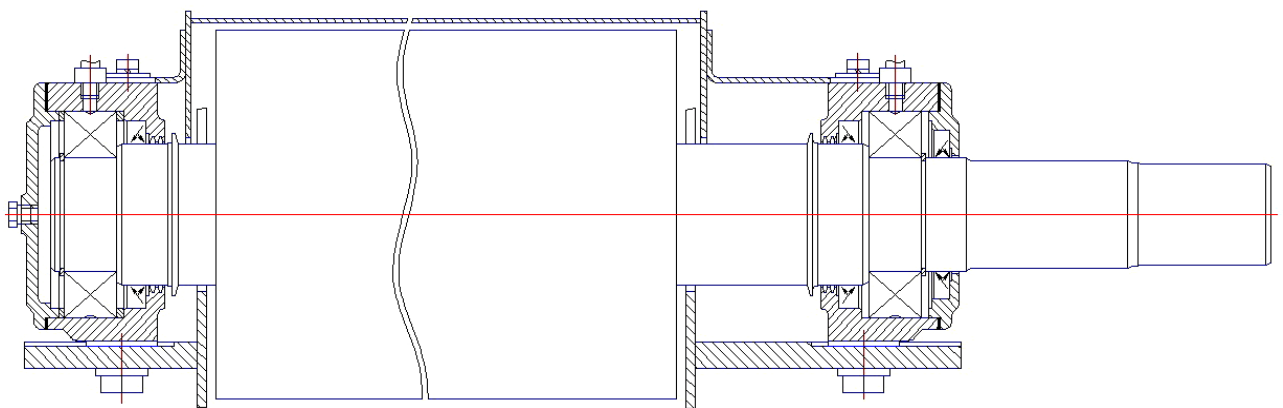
Схема установки валу доподрібнюючого пристрою
